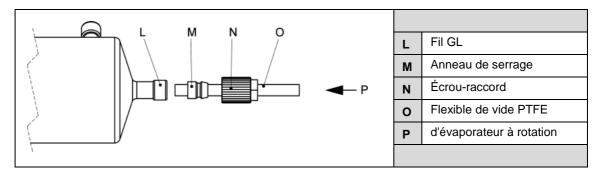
Indication pour un assemblage pour le raccord d'aspiration
